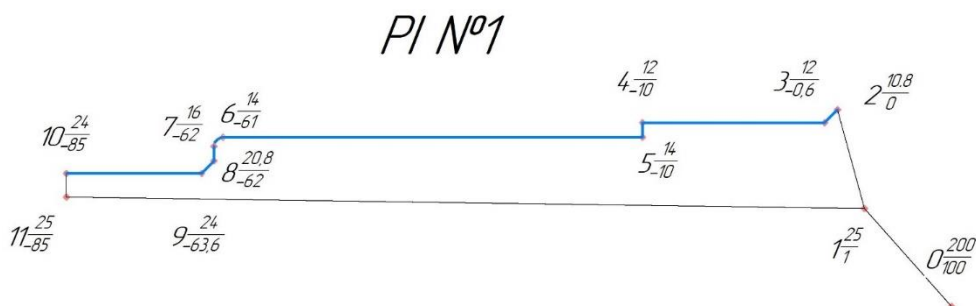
Траєкторія руху P11 на операцію 055 Токарна з ЧПК
